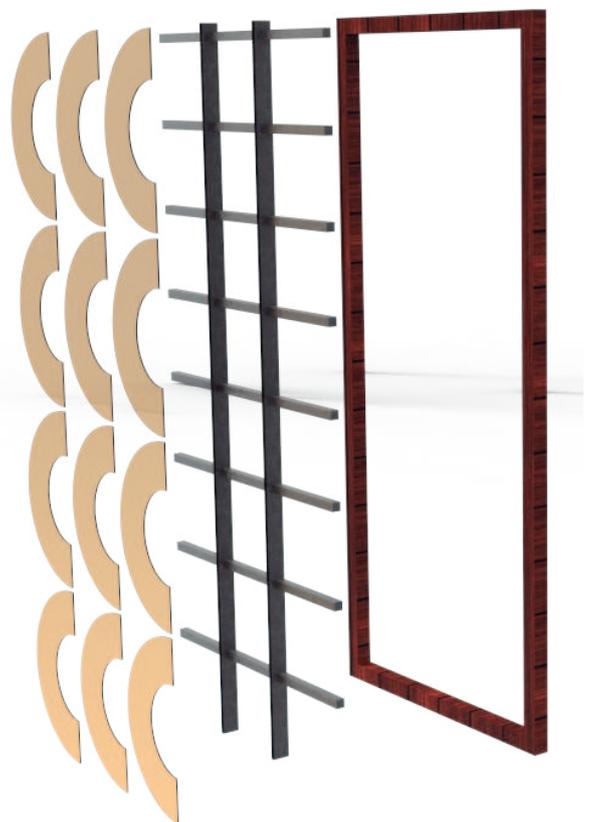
Esquema estrutural da aplicação do produto com elementos vazados
